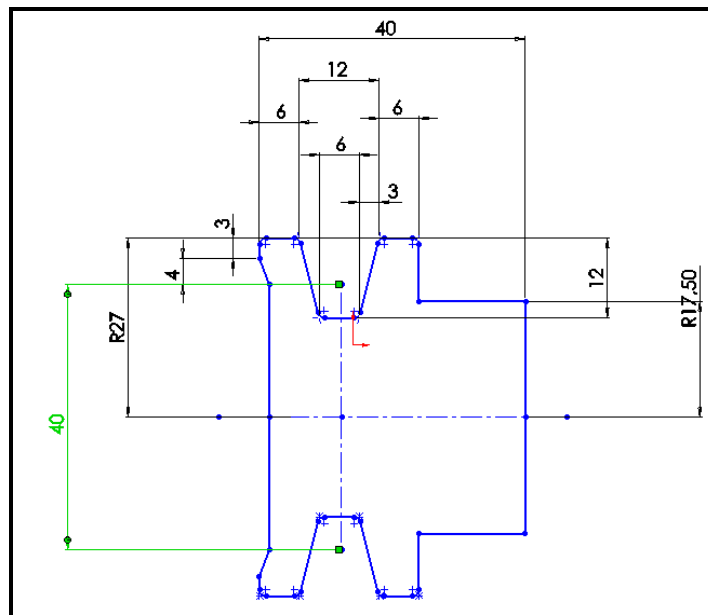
Dimensiones de la polea del motor y del ventilador
